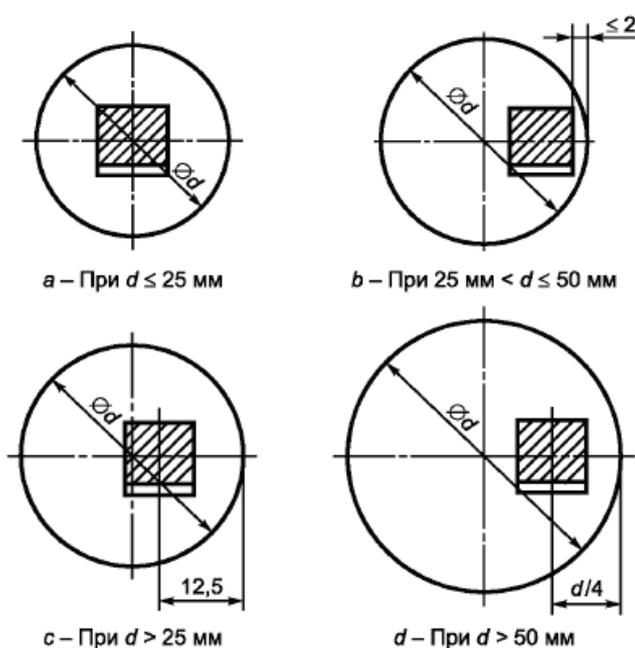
Сортовой прокат круглого сечения и катанка. Места вырезки заготовок для образцов (испытательных образцов) для испытаний на ударный изгиб (по ГОСТ 53845–2010)
